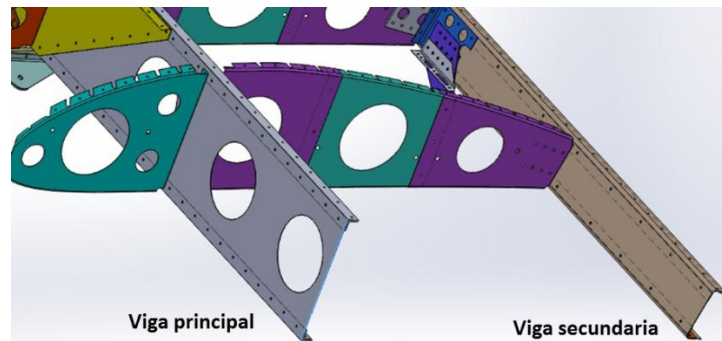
Detalle estructura del ala (Imagen suministrada por Aeroandina)
